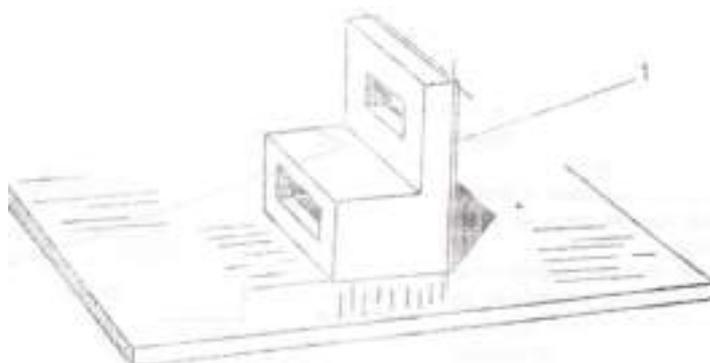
Colocação da peça para a traçagem de um plano perpendicular ao plano horizontal (1).
